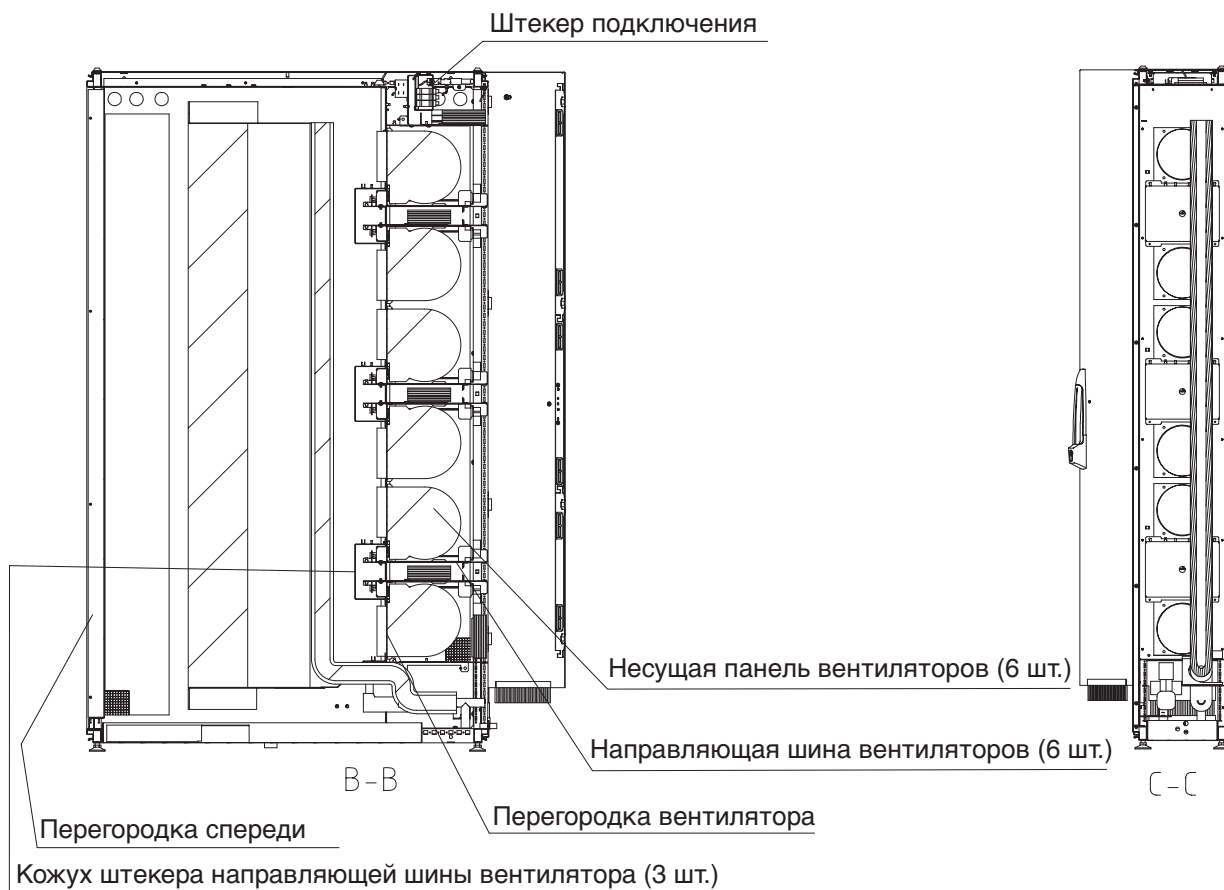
Обзорный чертёж – Liquid Cooling Package Plus EC (вид В и вид С)
